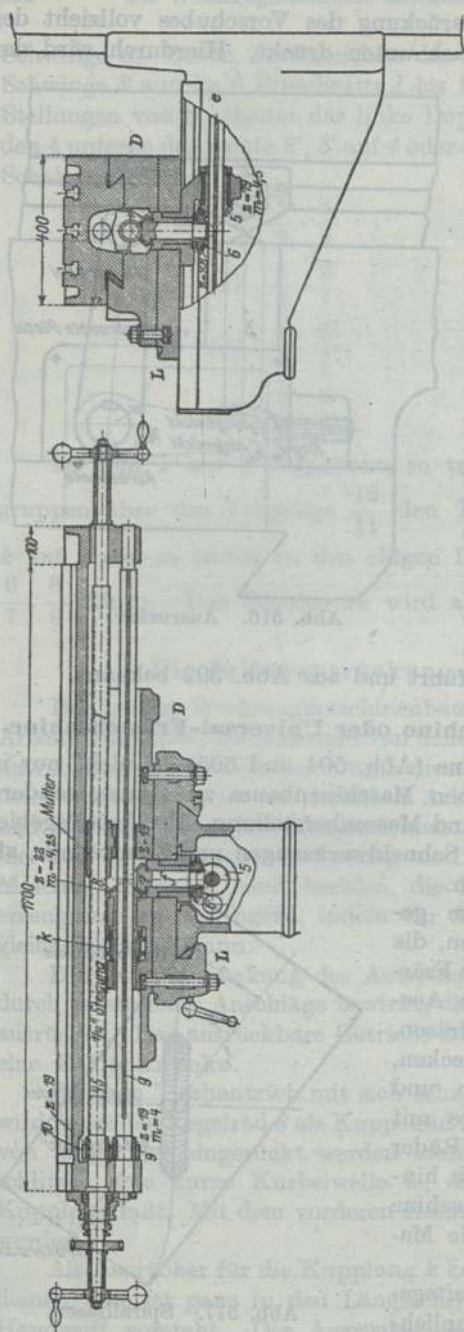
und 519. Arbeitstisch der Wanderer-Fräsmaschine.
